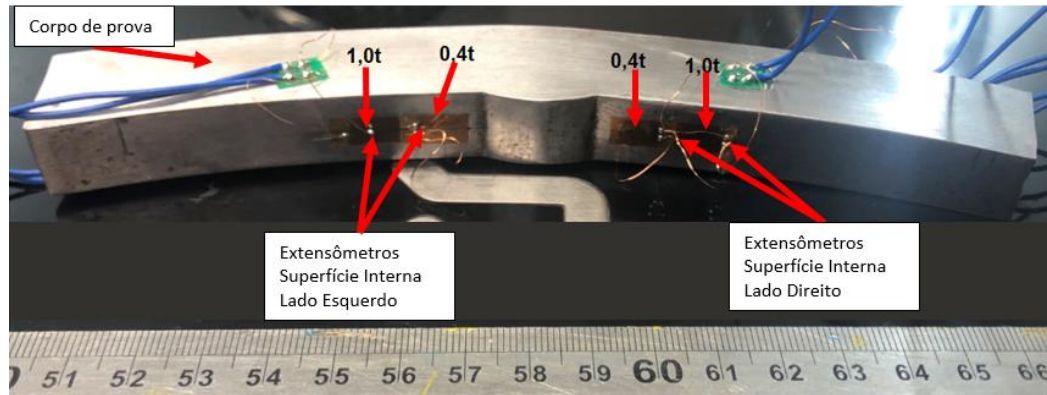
8 - Superfície inferior do corpo de prova com dois extensômetros instalados em cada lado da solda
